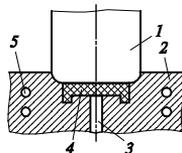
Рабочая часть пресс-формы для обычного (компрессионного) прессования:
